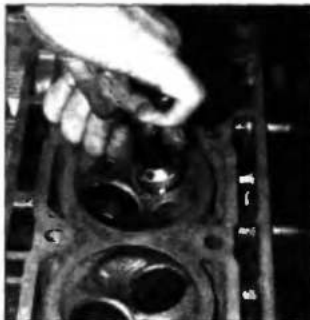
Ремонт седла клапана приспособлением с режущей головкой и неподвижным креплением пилота в направляющей втулке
